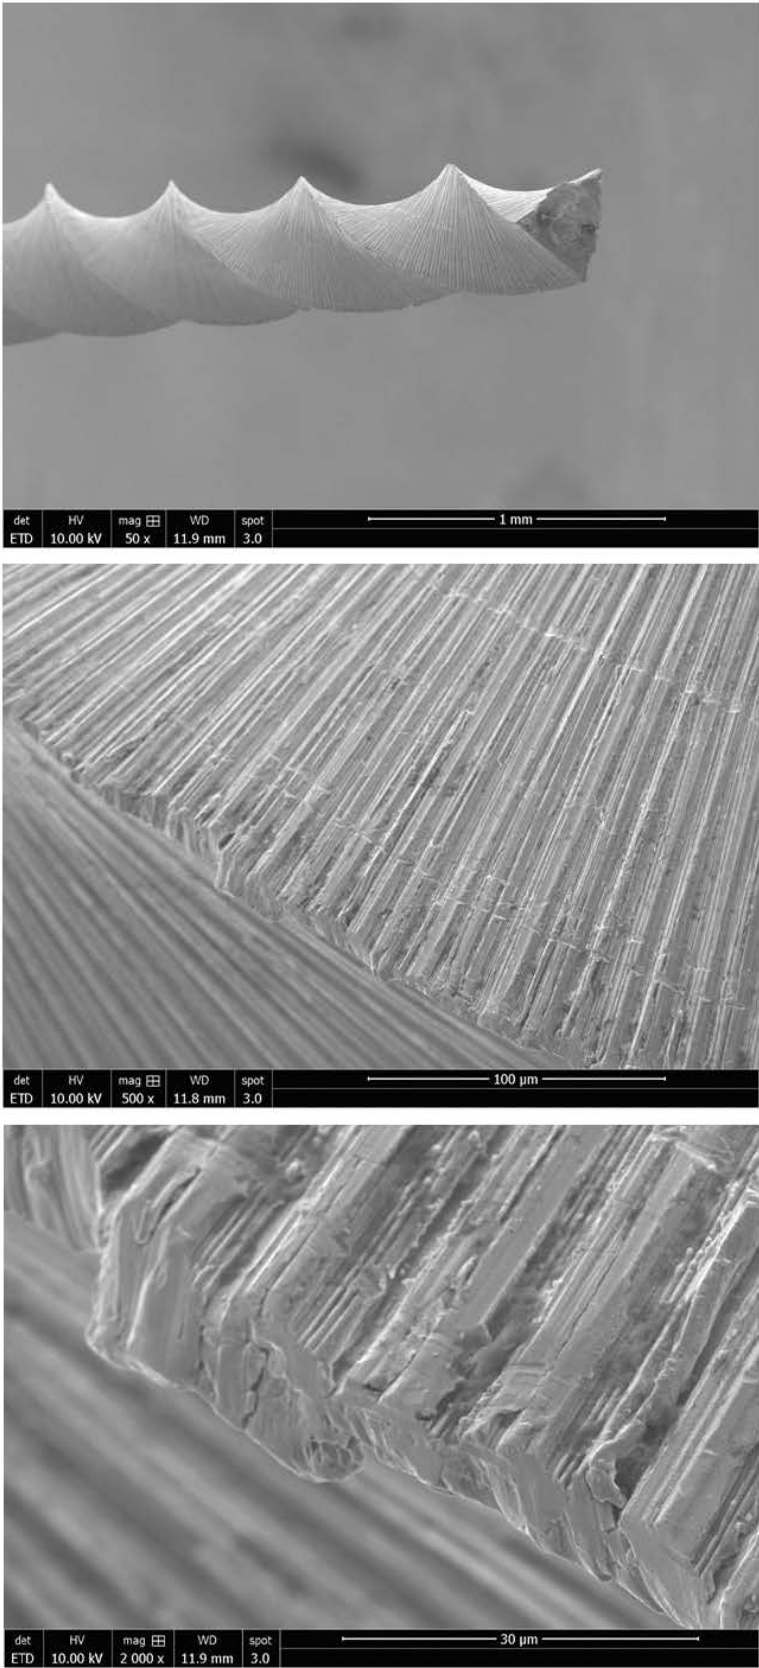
Stries d'usinage en surface des prototypes en CuAlBe monocristallin.
